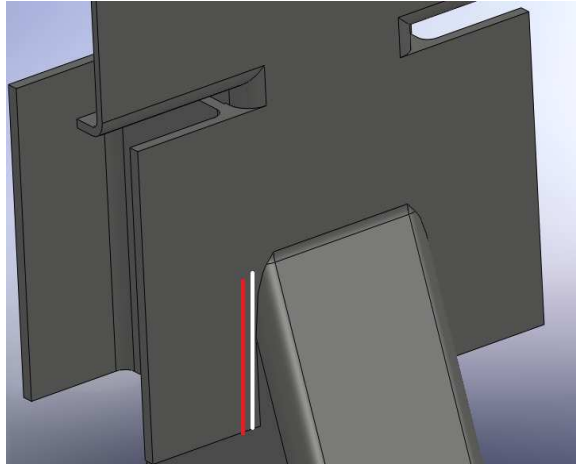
Localização da sobreposição dos cordões de soldadura
